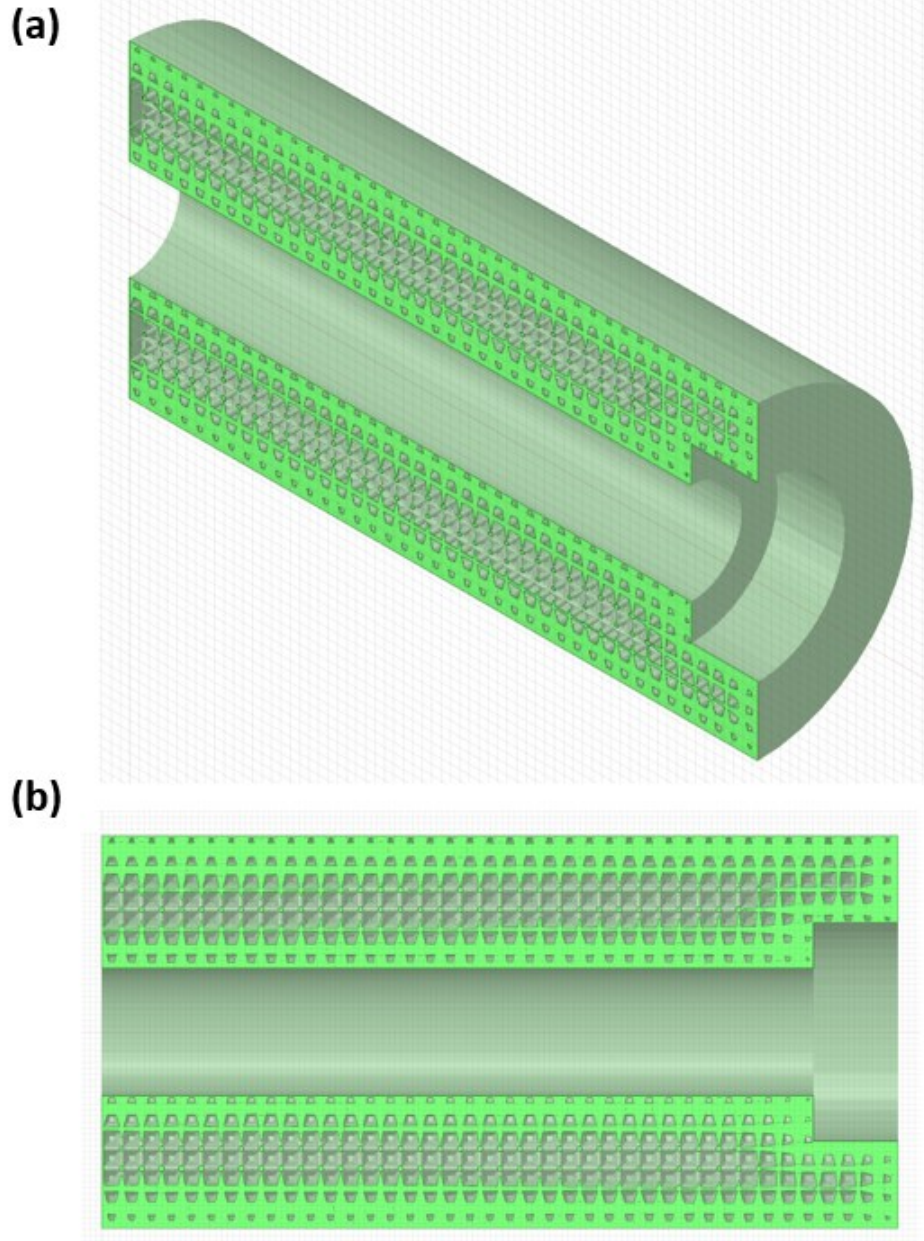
Renderização de estrutura reticulada com célula cúbica, tamanho 5 mm: (a) vista tridimensional em perspectiva, e (b) vista em corte.
